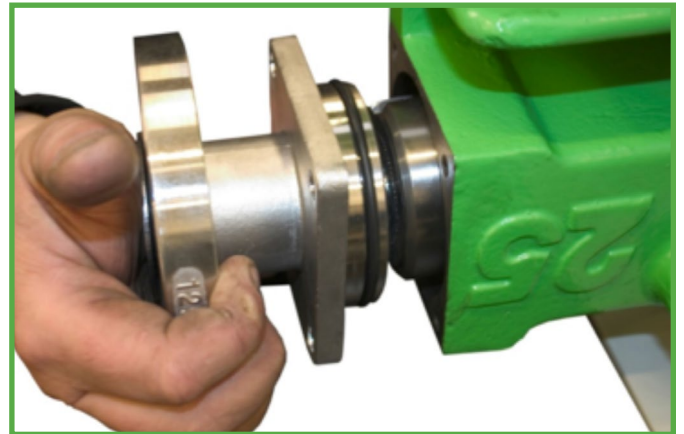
Einführung des Anschlussflansches & des Einsatzes
